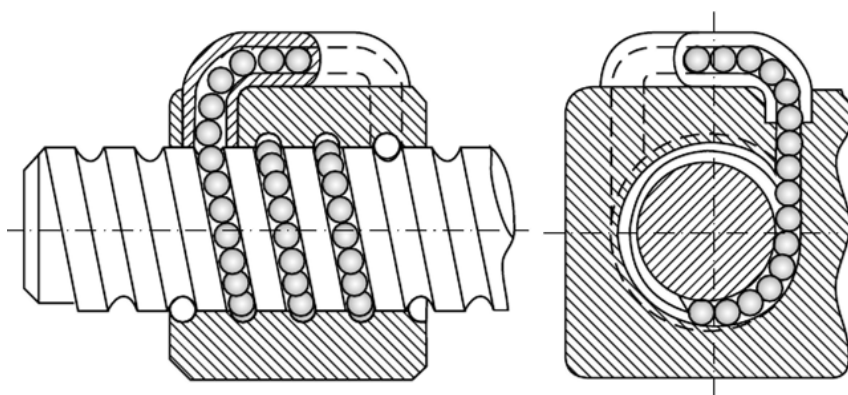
Шариковая передача винт-гайка с одинарной гайкой
